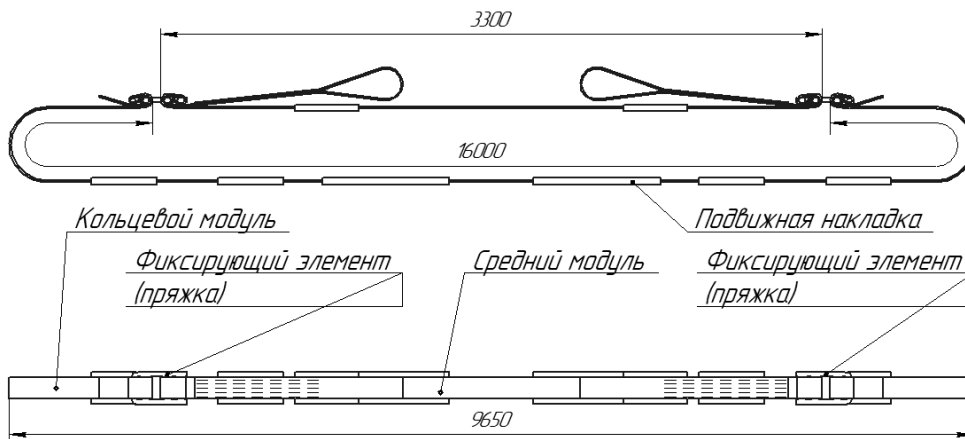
Общий вид крепления МВ КТБ4 5,0/16000-3300.
